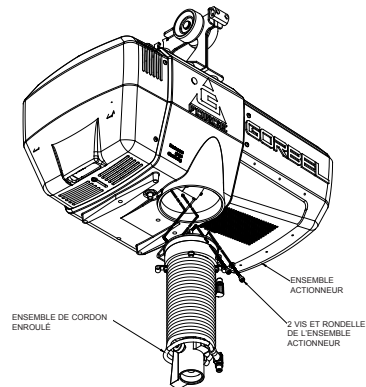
D. Installation de l'ensemble de cordon enroulé (vue de dessous).
